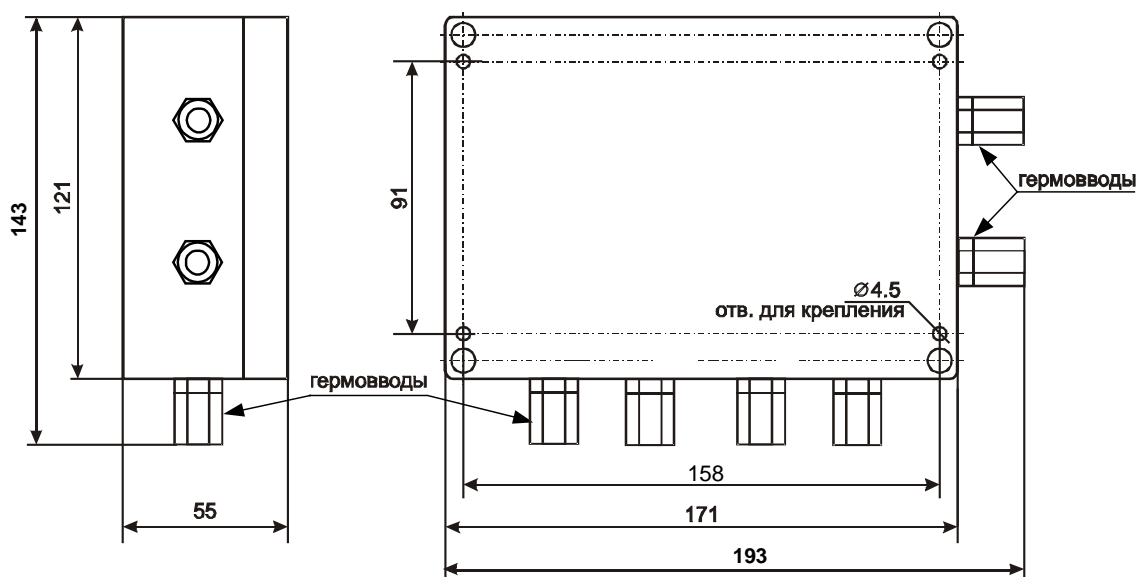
Габаритные и присоединительные размеры КА2, базовый вариант, исп. IP65
